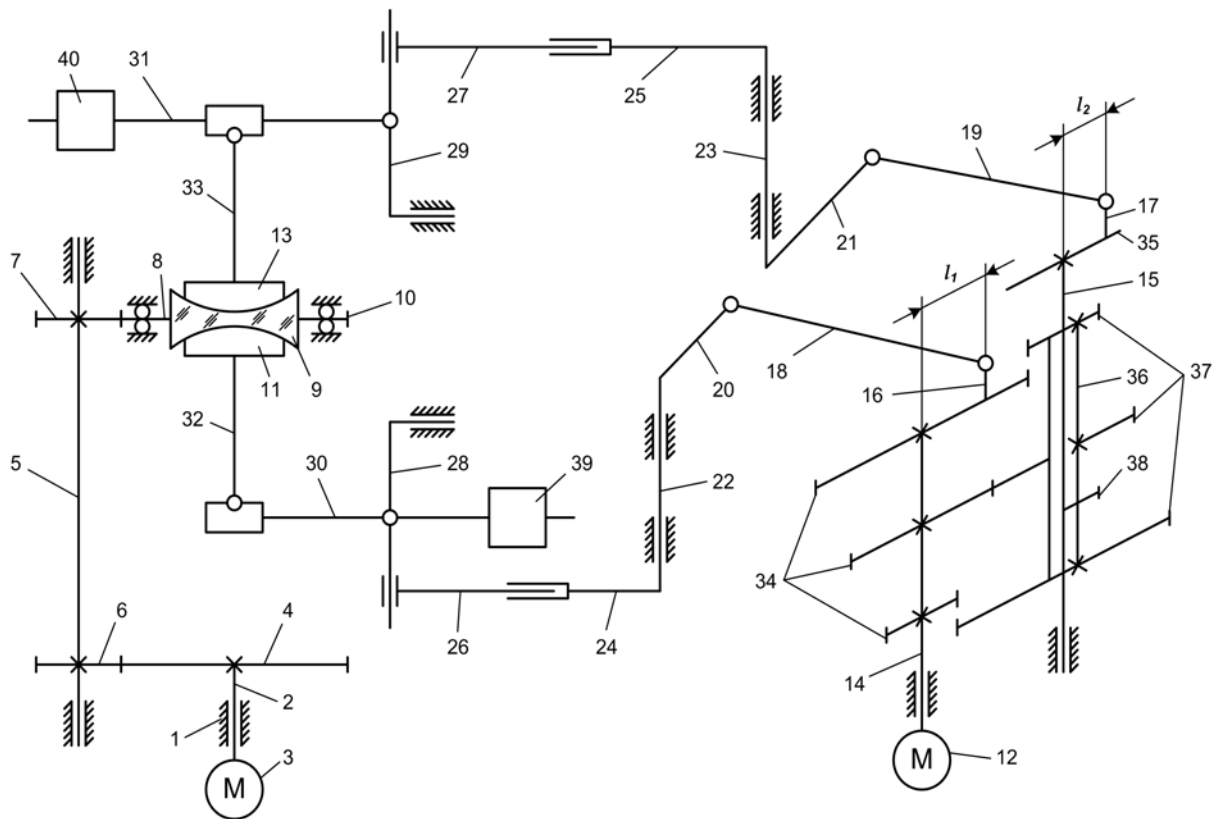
Схема станка для одновременной двусторонней обработки линз с крутыми вогнутыми поверхностями
